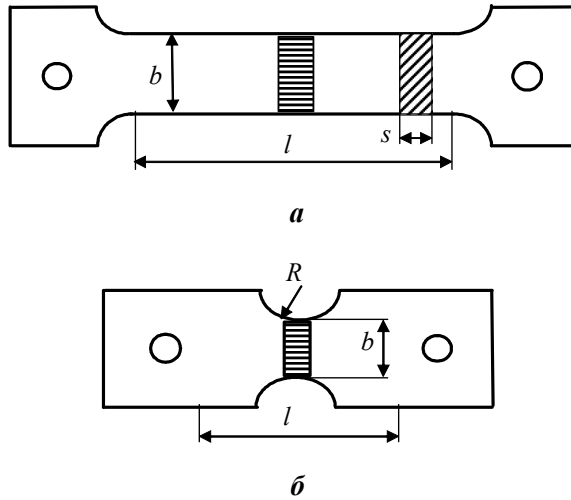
Зразки для випробувань зварного з'єднання на статичний розтяг:
